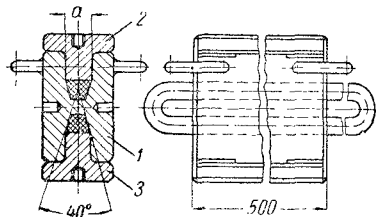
Круглая прессформа для изготовления клиновых ремней: 1 — матрица; 2 — пуансон; а — крестовина для обеспечения жесткости пуансона; б — уши.
